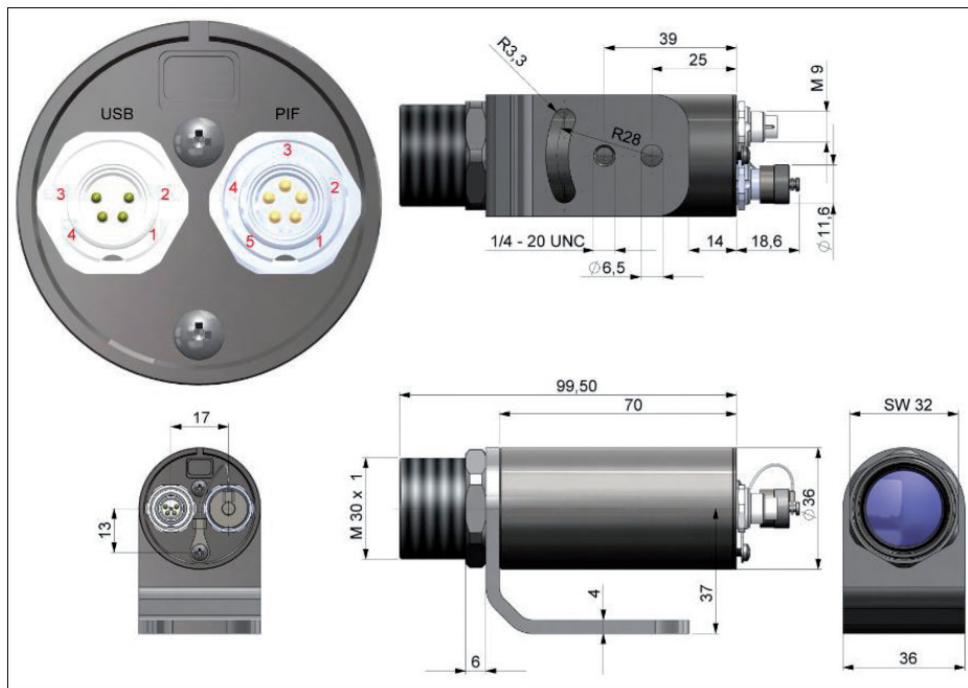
Maßzeichnung thermoMETER TIM 40, Abmessungen in mm
